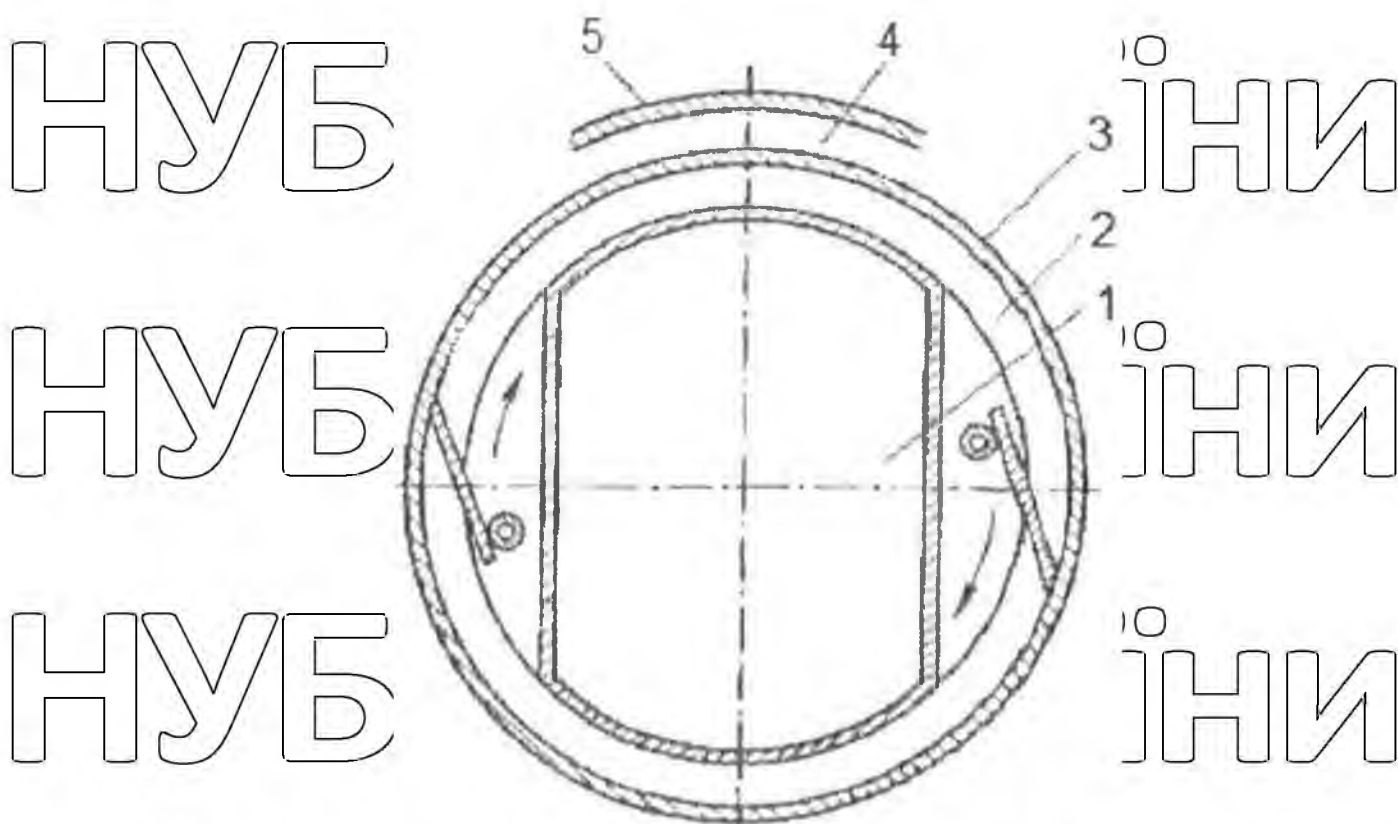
Схема циліндра: 1 – барабан-витискувальний; 2 – робочий простір; 3 – циліндр; 4 – кільцевий канал для холодоагенту; 5 – рубашка
